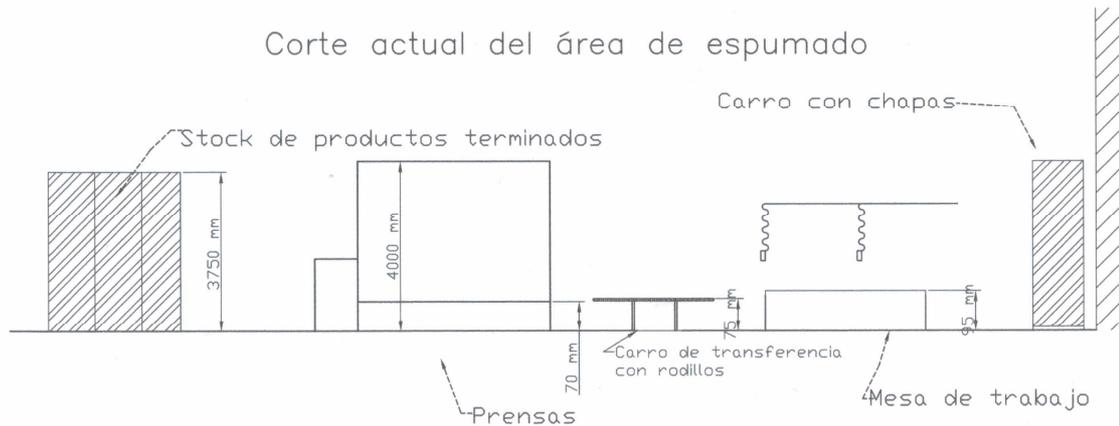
Corte del sector de espumado con la mesa de rodillos.
